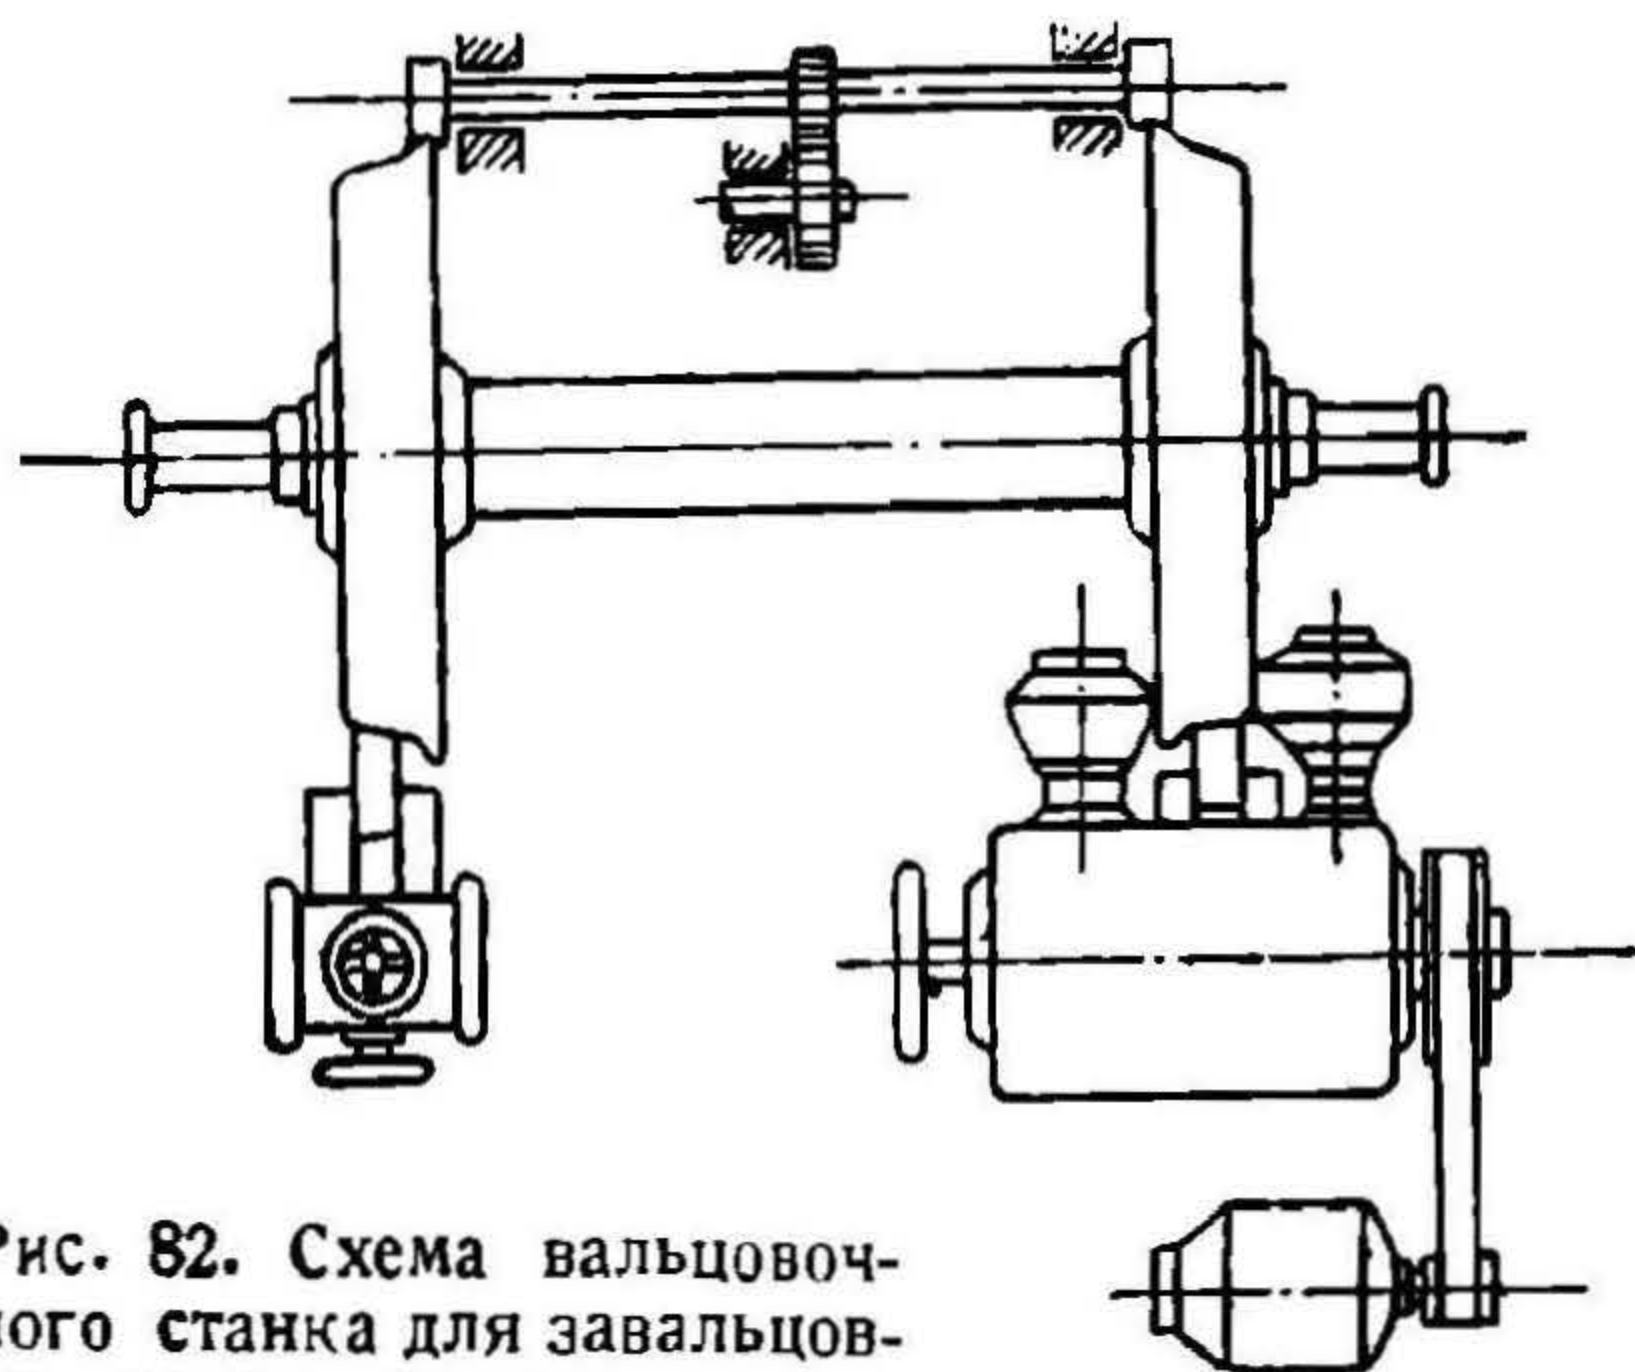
Схема вальцовочного станка для завальцовки колец русско-германского способа крепления бандажей.
